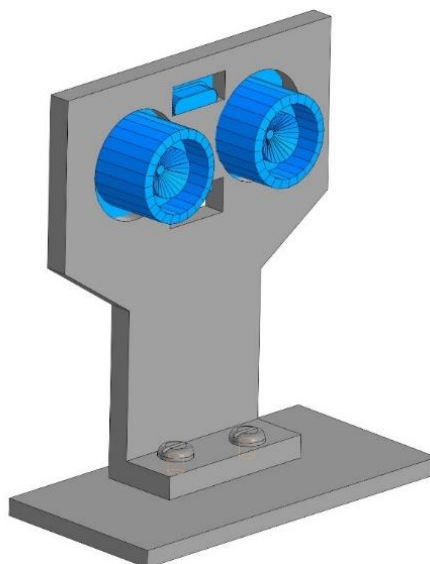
Внешний вид 3D-модели крепления ультразвукового датчика HC-SR04
